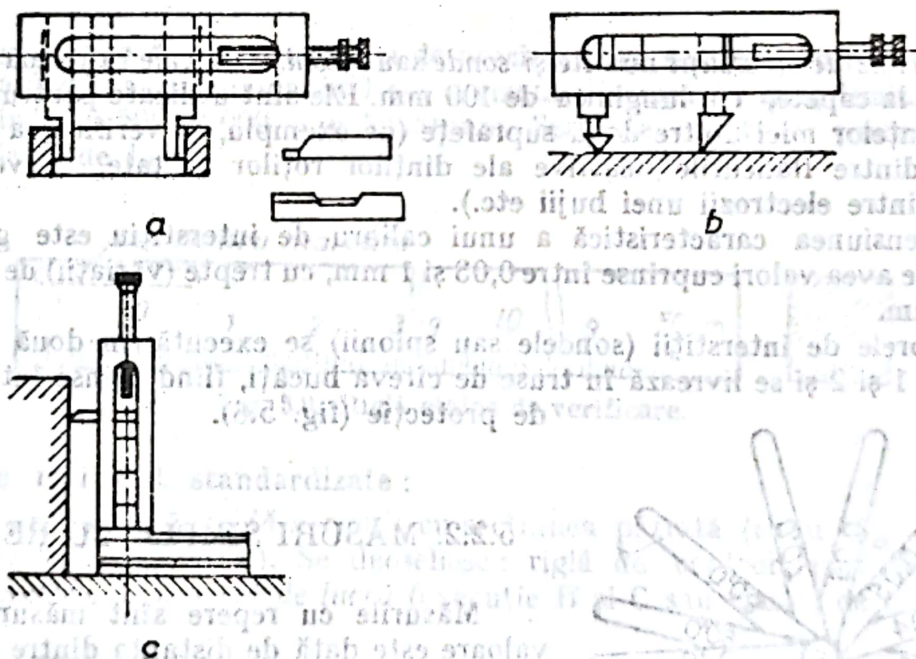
Dispozitive de măsurare cu cale plan-paralele :
